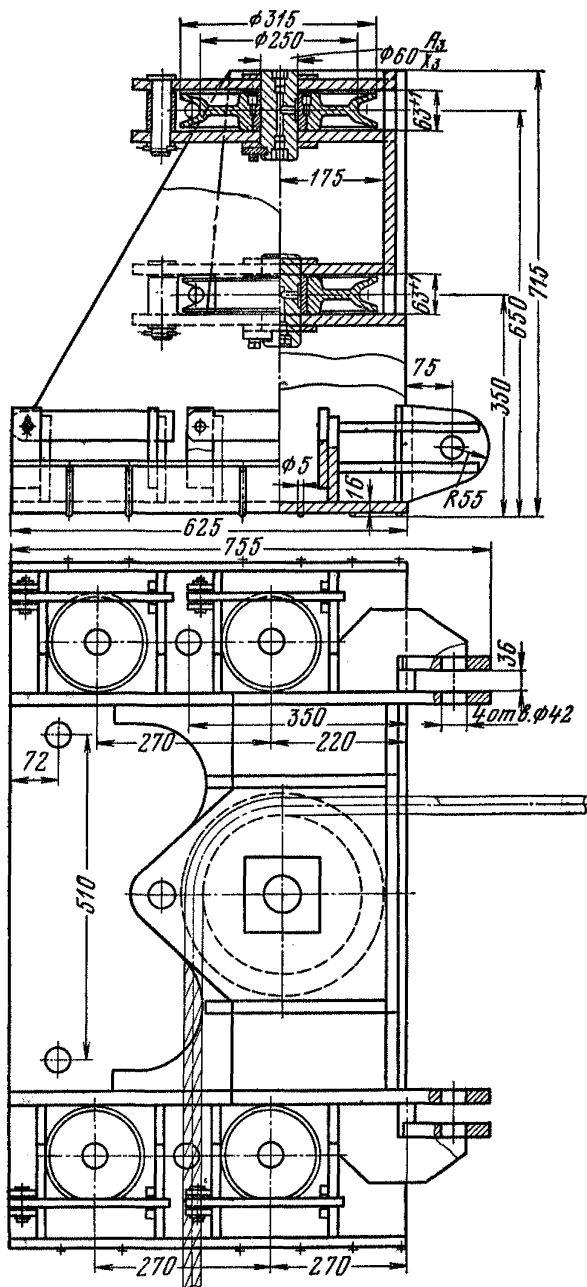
Устройство для крепления обводного блока предохранительного каната
